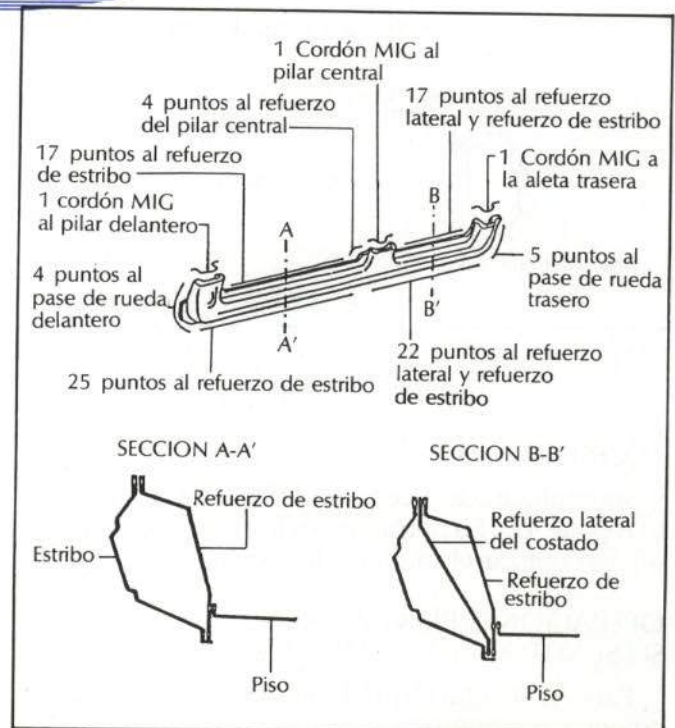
Ensamblado y secciones del estribo bajo puertas.
